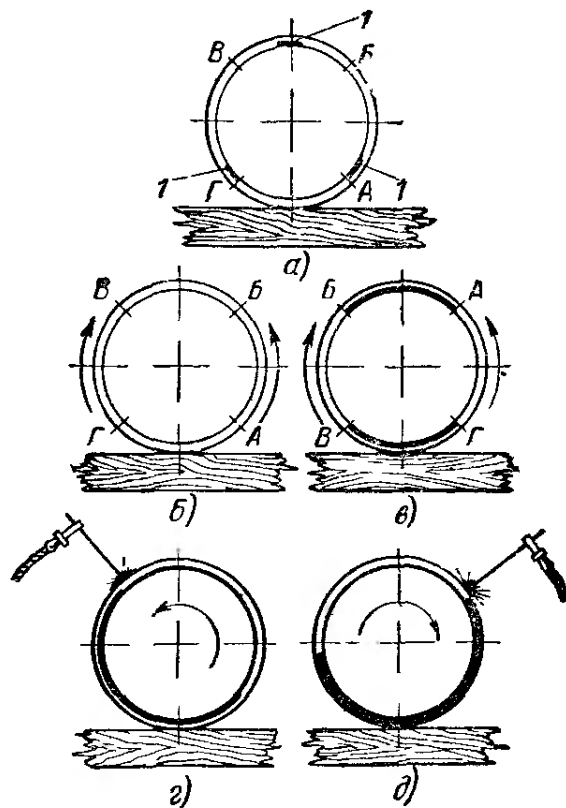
Порядок сварки стыков труб с поворотом
